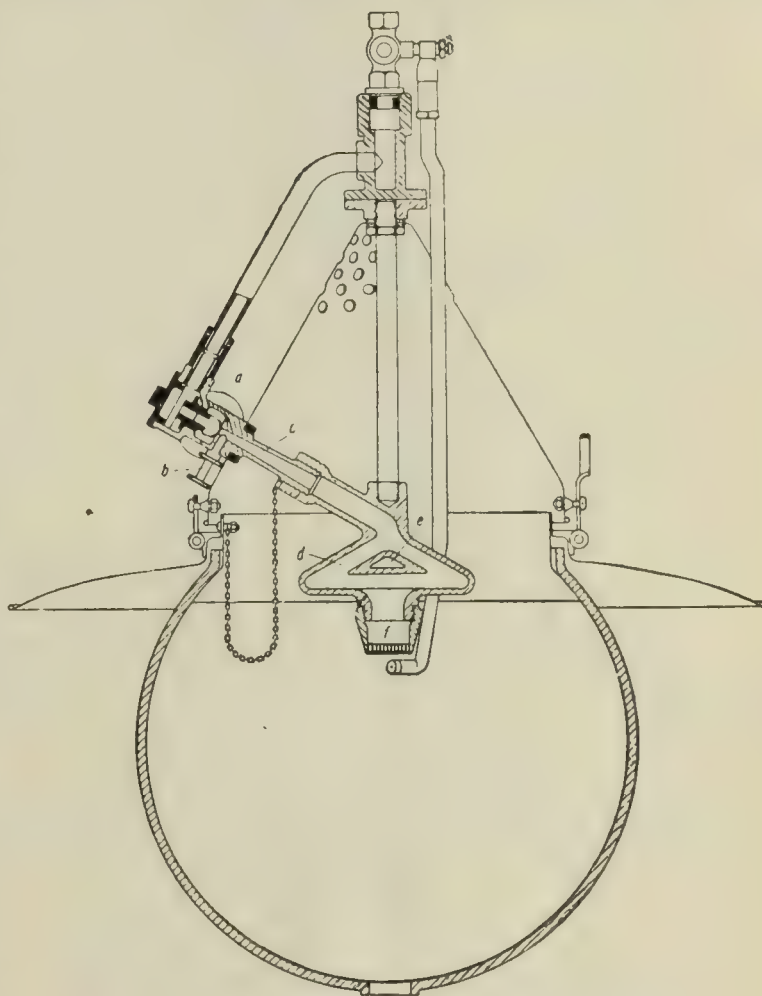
Preßgaslampe für Innenbeleuchtung.
